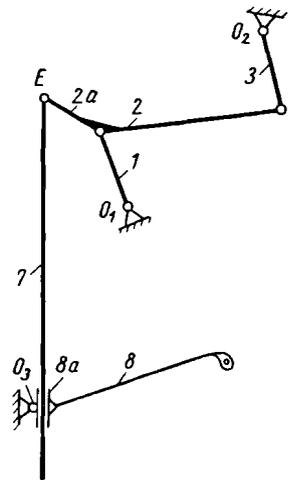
Схема механизма нитепритягивателя машины 236-го класса
